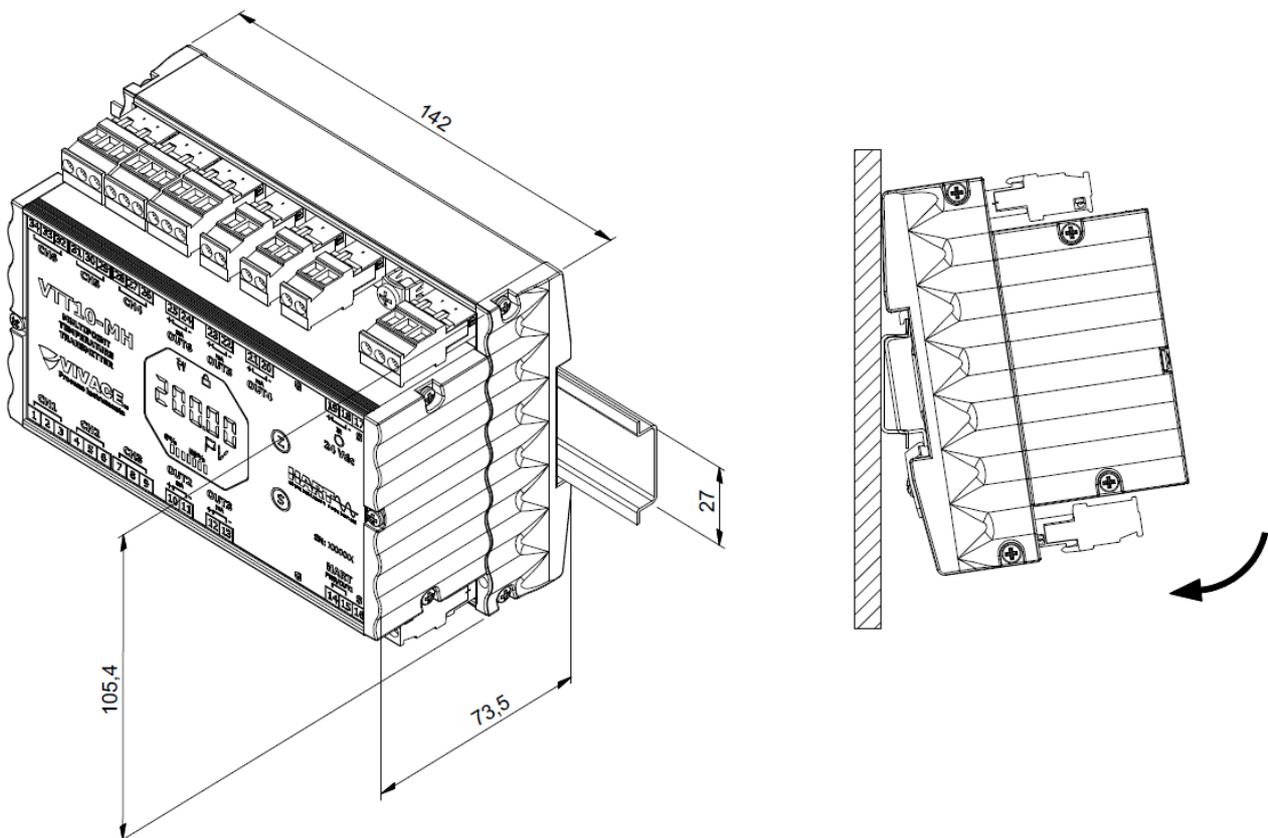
Diseño dimensional y esquema de montaje del VTT10-MH.
